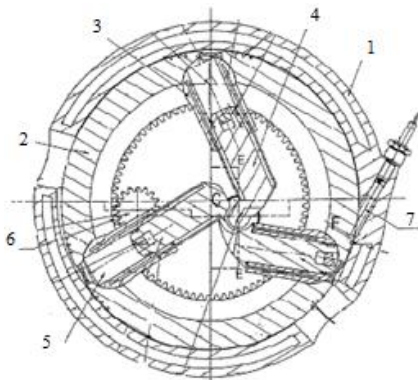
Конструктивна схема роторно-поршневого двигуна [2]: 1 – корпус; 2 – ротор; 3 – циліндр; 4 – поршень; 5 – робоча камера; 6 – зубчатий вінець; 7 – камера згоряння
